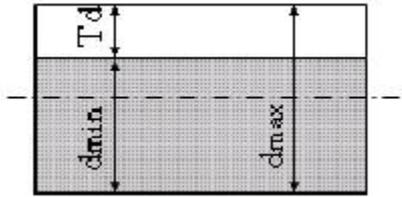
Предпочтительное изображение вала,  $Td$  – допуск на диаметр вала
